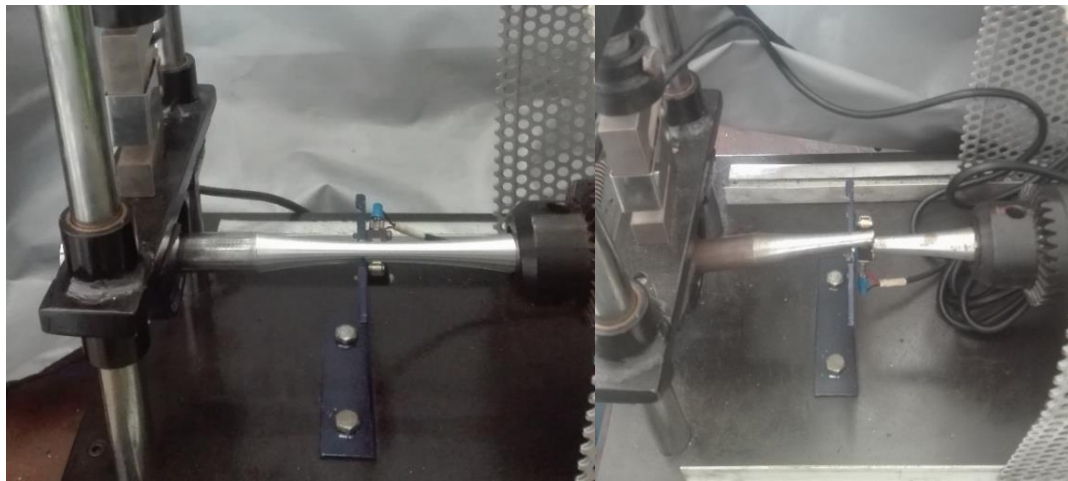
Montaje y fractura de una probeta en la máquina de ensayo de fatiga.
